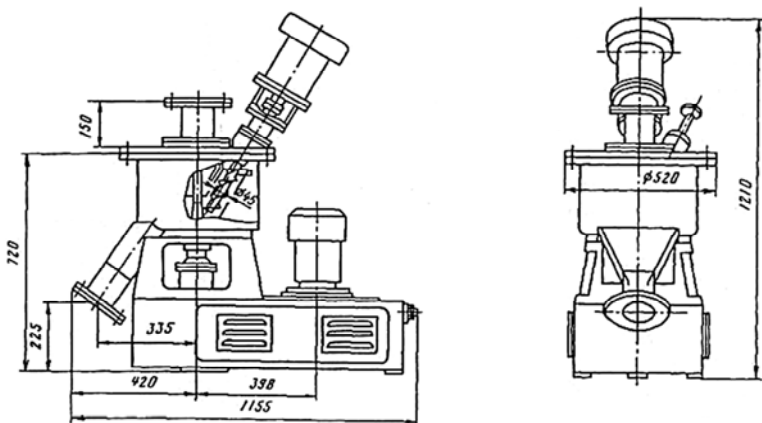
Центробежный смеситель НДЦ-25 ВБК-01
